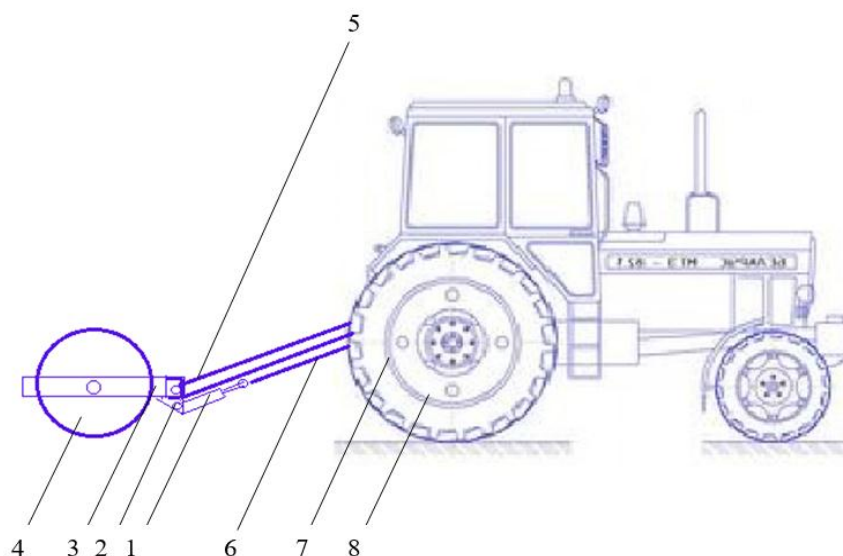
Принципиальная схема прикатывающего агрегата с установленным догружающим устройством: 1- гидроцилиндр; 2-опорный кронштейн; 3-рама катка; 4- каток; 5- сница; 6- гибкая тросовая связь; 7- крепёжный кронштейн; 8- трактор
